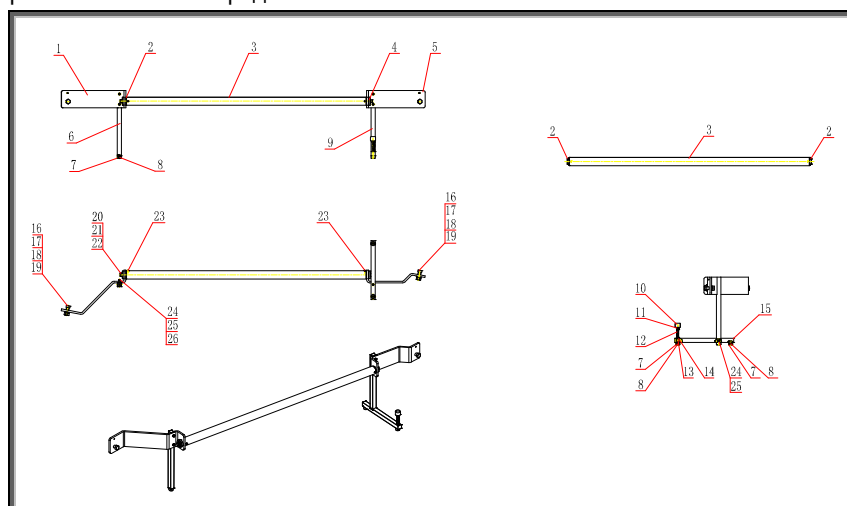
Рисунок порядка сборки калибровочной системы
